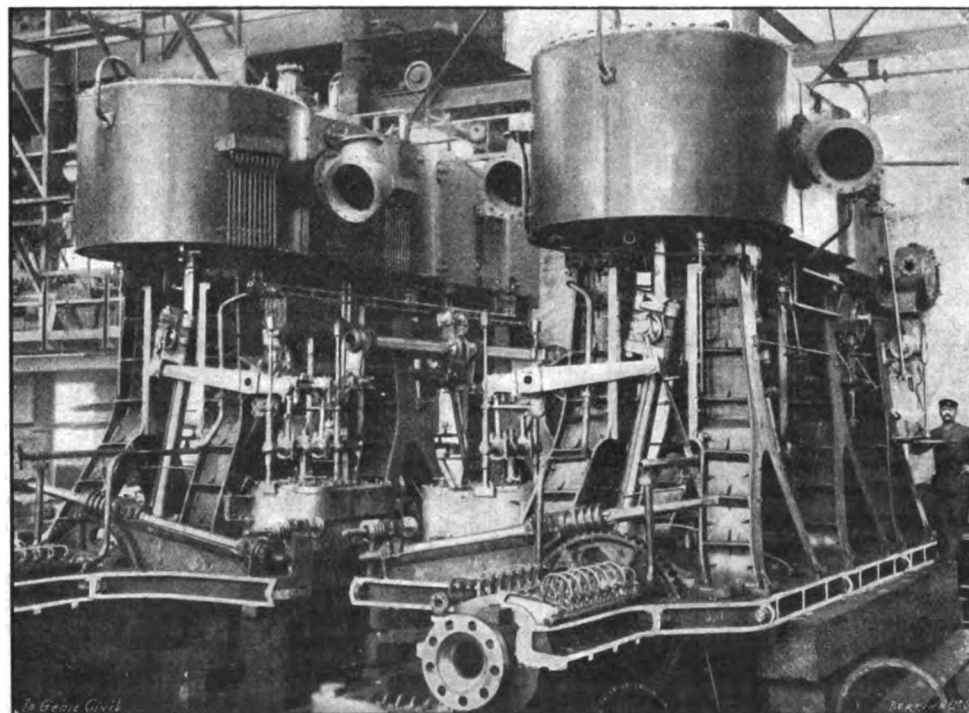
MACHINES DU « NOORD BRABANT » : Vue en bout des deux machines.
